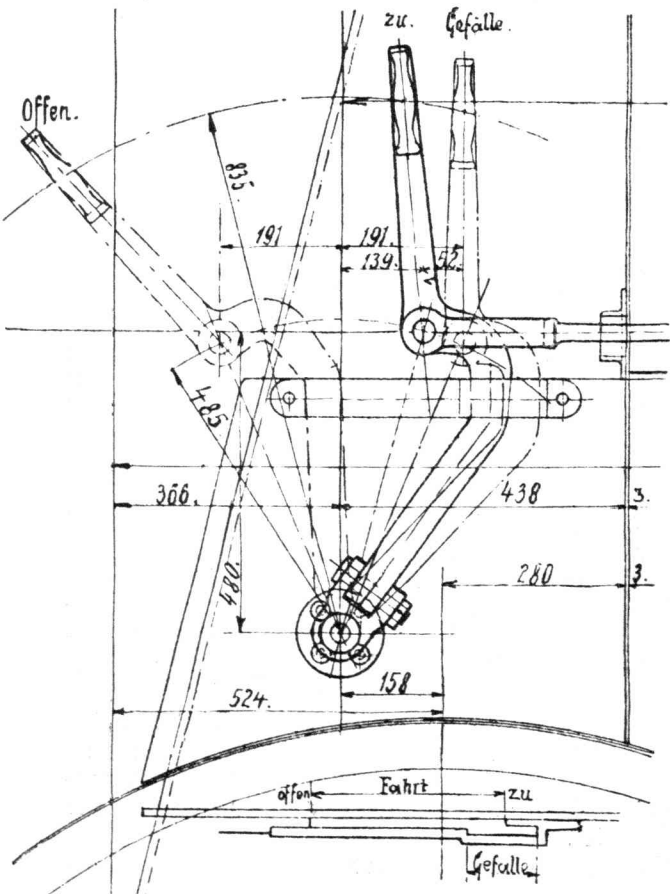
Reglerquadrant mit Umschalteneinrichtung für die Fahrt auf Gefällen.
